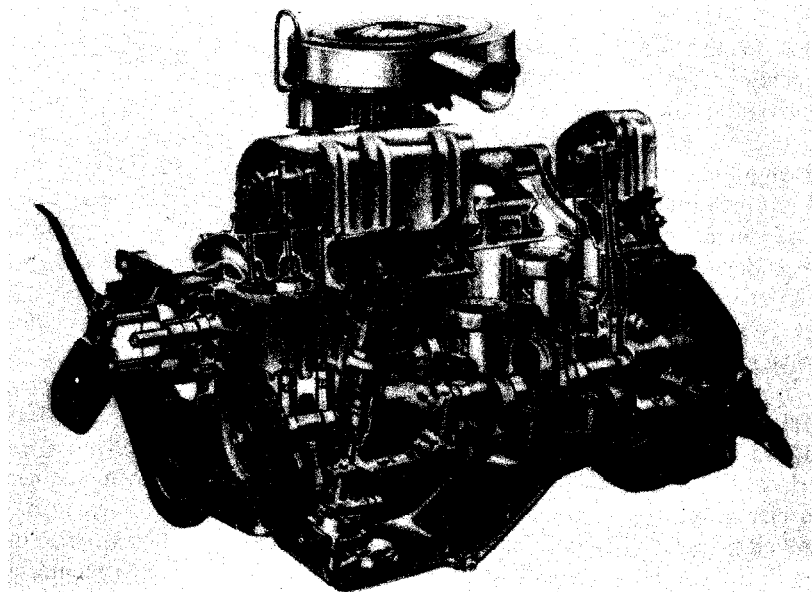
Sección de un motor de seis cilindros en línea inclinados con válvulas en culata. Los cilindros están inclinados para obtener menores alturas del motor (Dodge Division of Chrysler Motors Corporation). ▲
